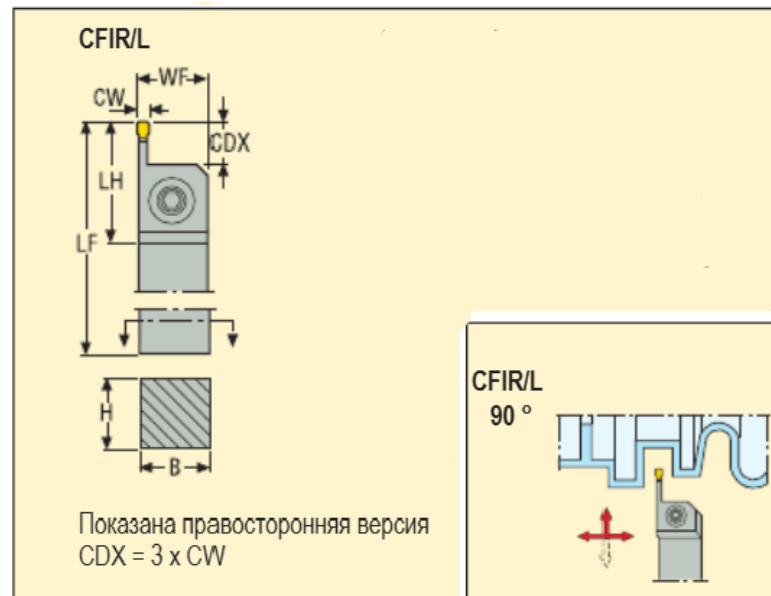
Державка CFIL3225P05 [1. с.626]
